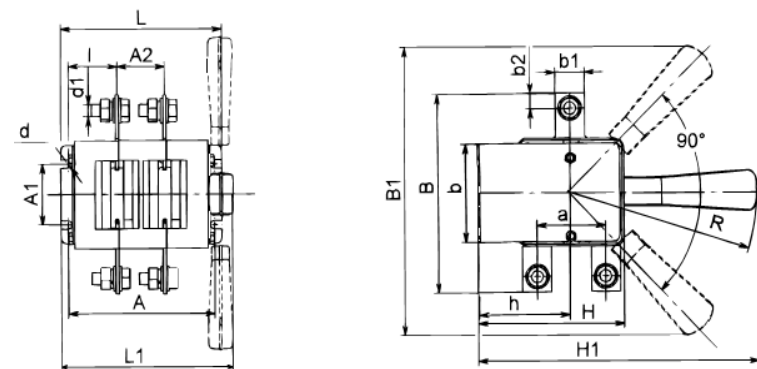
Б Выключатель-разъединитель на два направления двухполюсный с боковой рукояткой.
